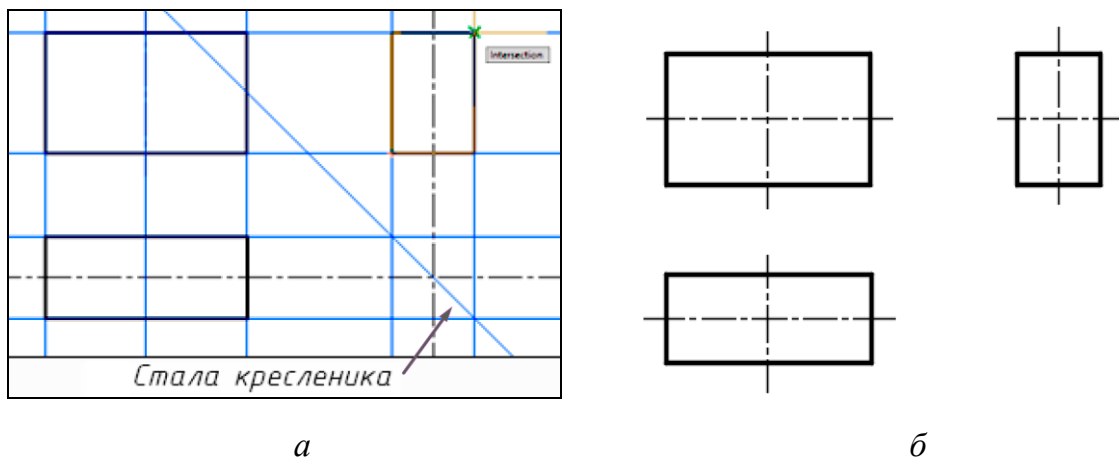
Побудова проєкційного кресленика, допоміжний шар:
